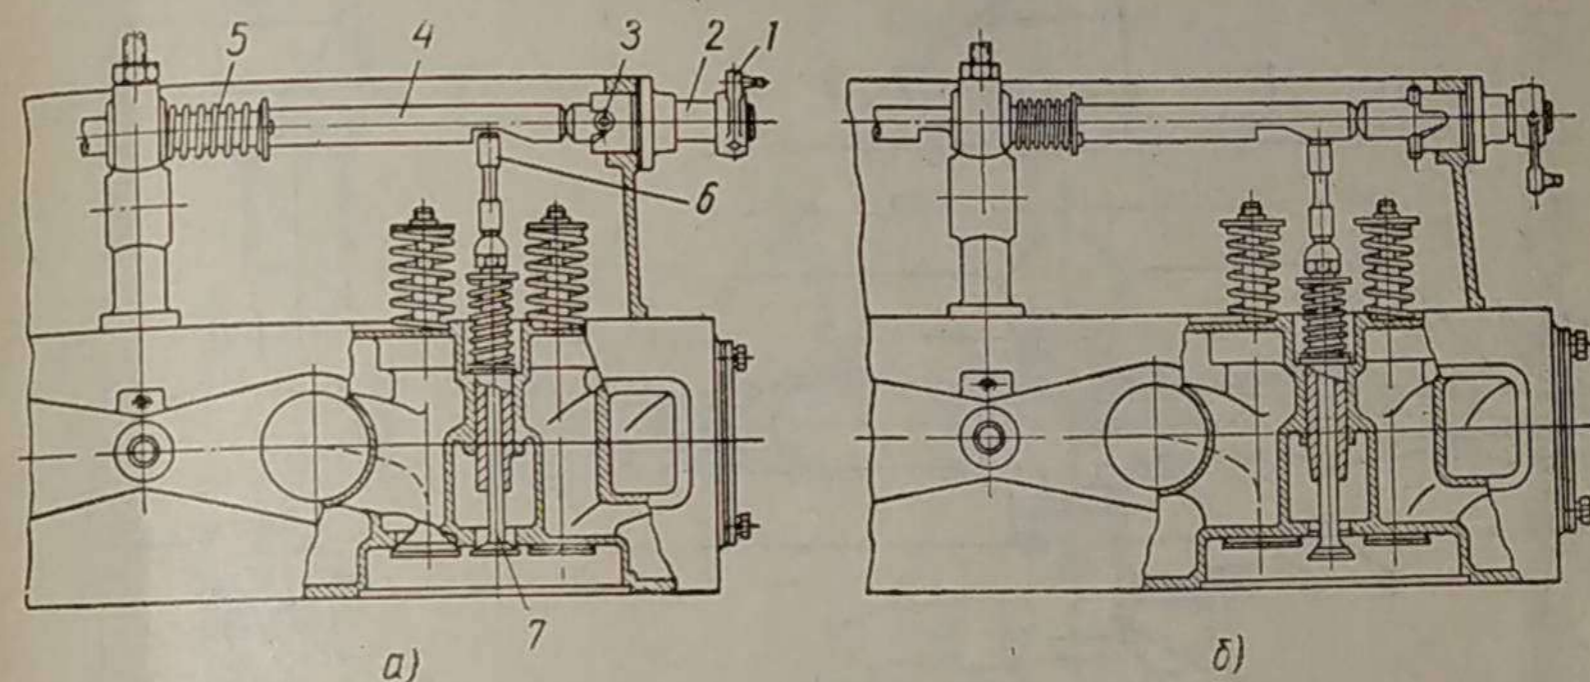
Головка цилиндров двигателя Д 2Г:
